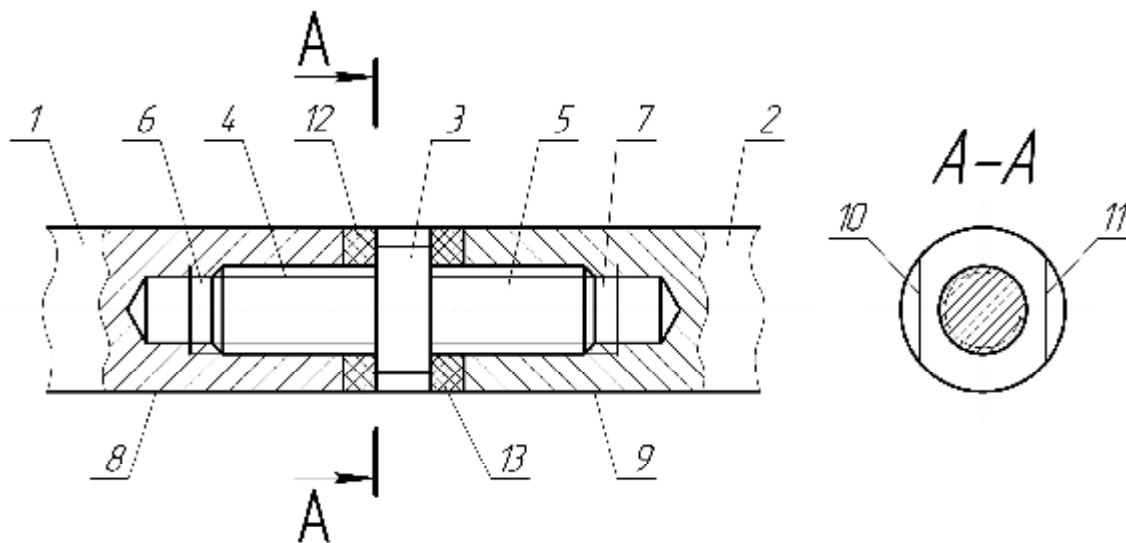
Схема різьбового з'єднання валів з засобом для з'єднання та фрикційними шайбами: 1 – ведучий вал; 2 – ведений вал; 3 – засіб для з'єднання валів; 4, 5 – різьбові стержні; 6, 7 – різьбові отвори; 8, 9 – поверхні відповідно ведучого та веденого валів; 10, 11 – лиски; 12, 13 – фрикційні шайби
